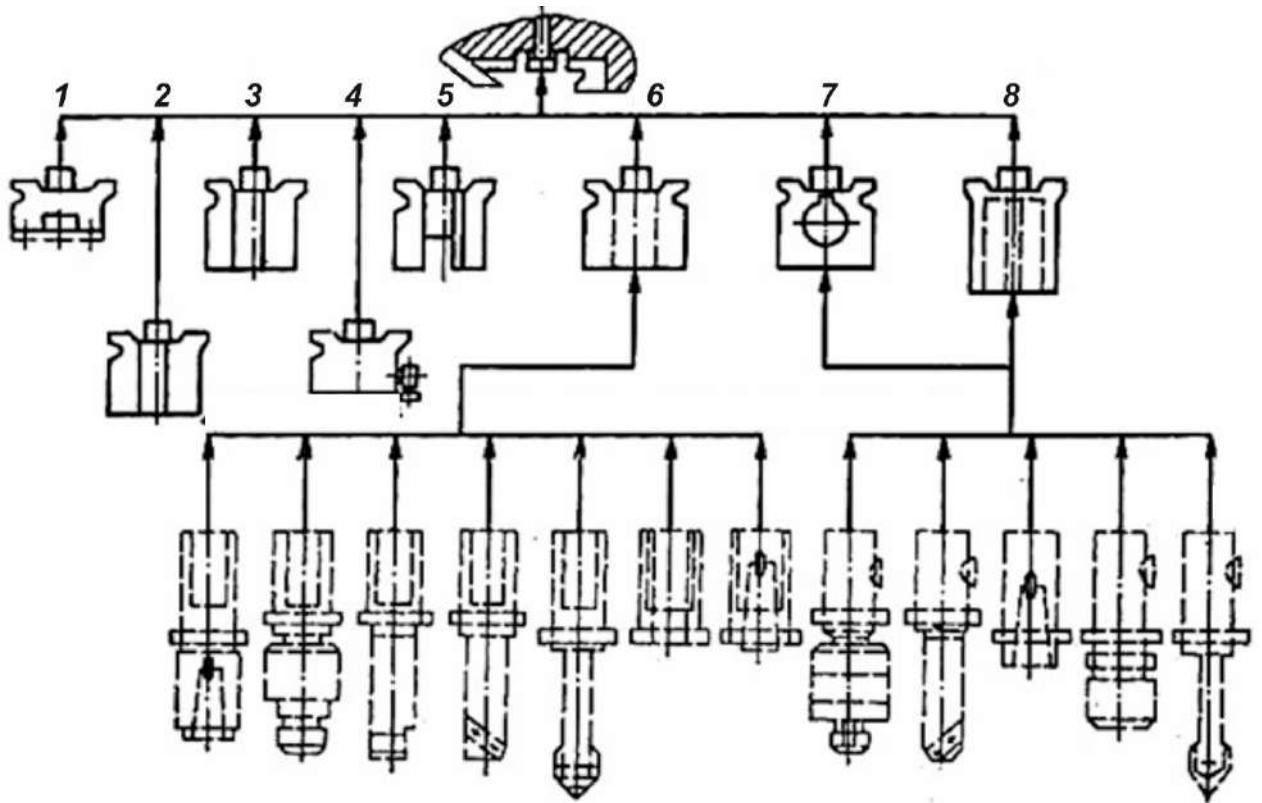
Інструментальна система токарного верстата з призмою, що базує.
